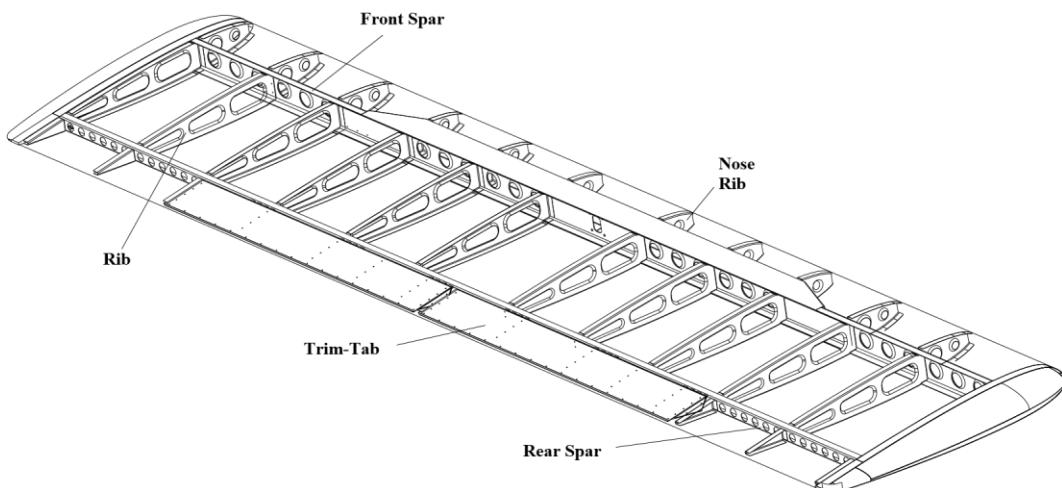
STRUCTURE DU PLAN HORIZONTAL
